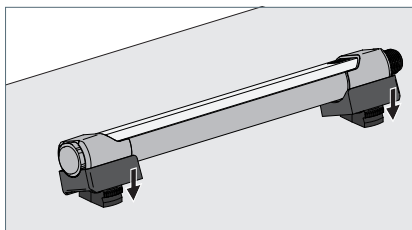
Montare l'apparecchio d'illuminazione sugli elementi di fissaggio.
